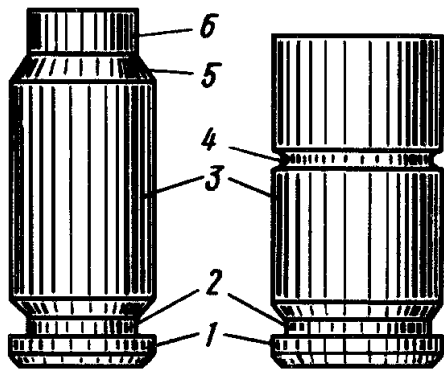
Гильзы унитарных патронов бутылочной и цилиндрической формы: 1 – шляпка; 2 – круговая выточка; 3 – корпус; 4 – канелюра; 5 – скат; 6 – дульце
